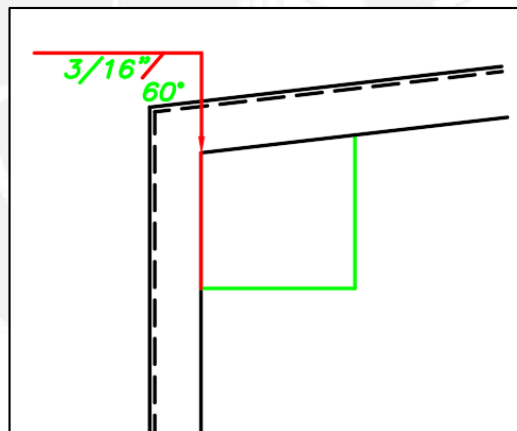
SIMBOLOGÍA DE JUNTA SOLDADA ENTRE CARTELA Y MONTANTE
